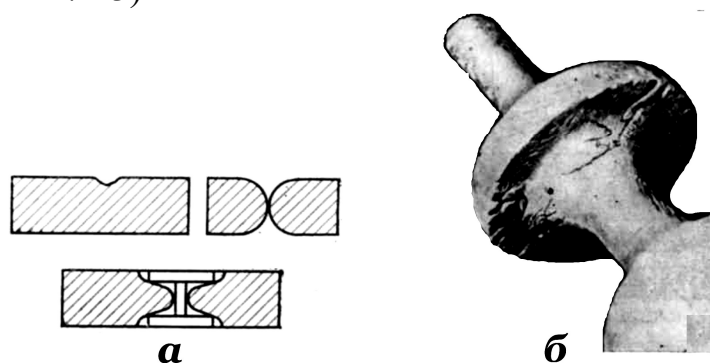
Дефект – спай: а – схема; б – дефектная отливка
